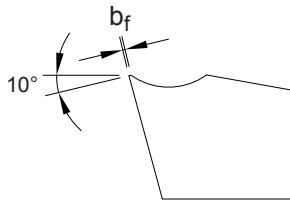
Neutrale openingshoek voor afwerking en voorbereiding
